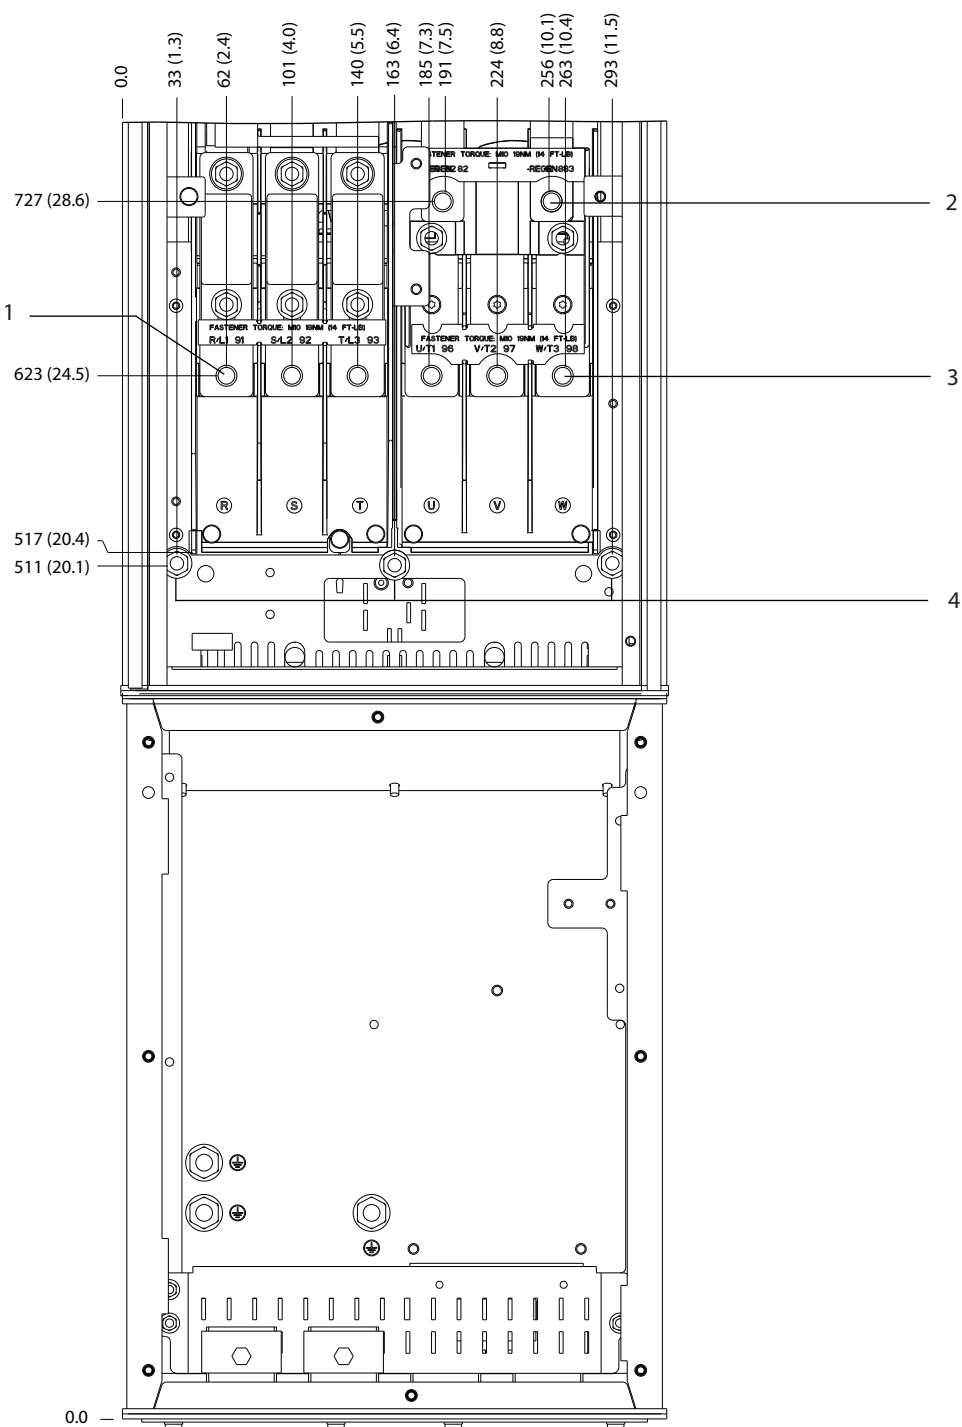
Dimensions des bornes D5h avec option sectionneur (vue frontale)
